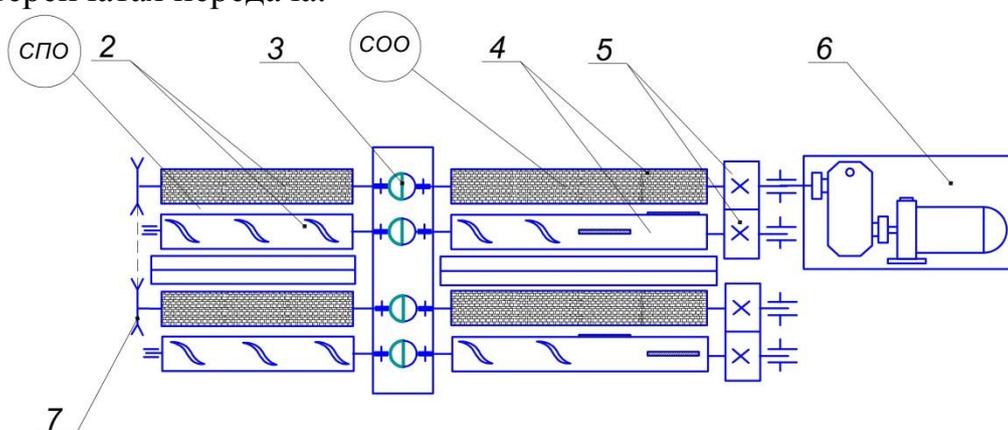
Конструктивно-технологическая схема блока валцов очистителя (вид сверху): 1-шкивы привода валцевого механизма; 2-комплект валцов предварительной очистки; 3-карданная передача; 4-комплект валцов основной очистки; 5-комплект шестерен привода валцевого механизма; 6-приводная станция.
